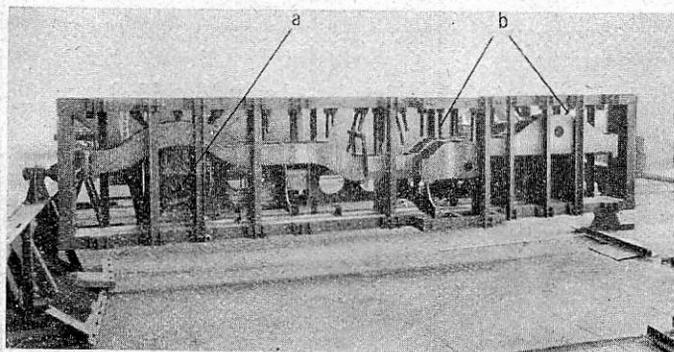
Drehgestellwange in drehbarer Schweißvorrichtung.
